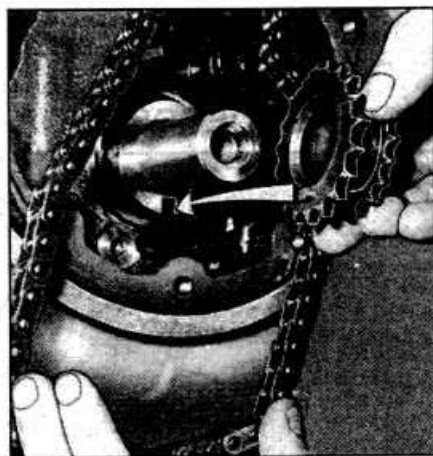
Установка звездочки на коленчатый вал, установленный в положение, соответствующее нахождению поршня 1-го цилиндра в ВМТ конца такта сжатия
